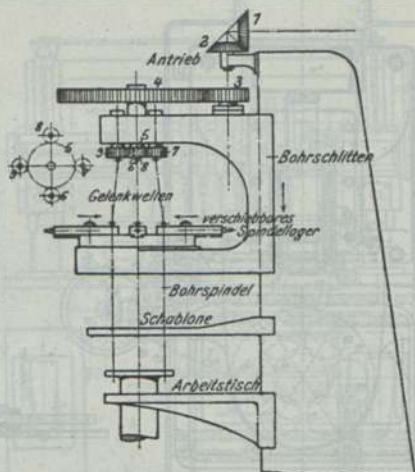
und 445. Plan einer Flanschenbohrmaschine.
